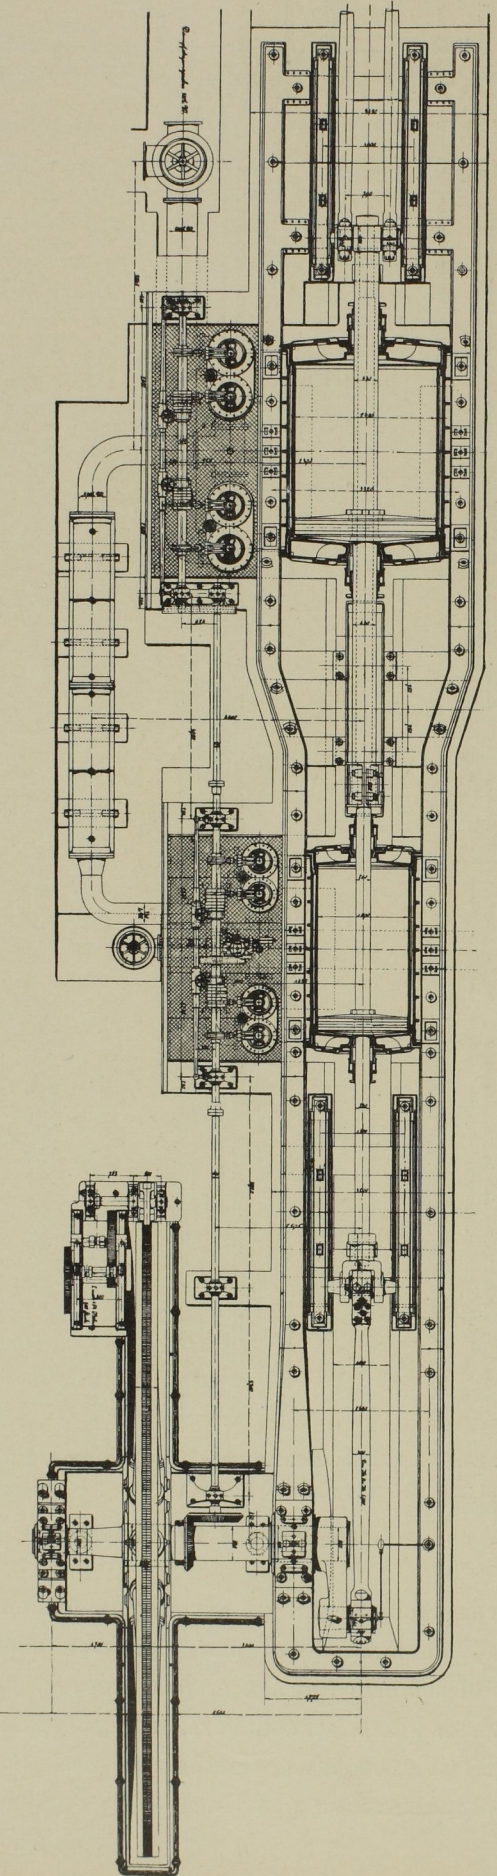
Grundriss der Maschine. Massst. 1:125.
